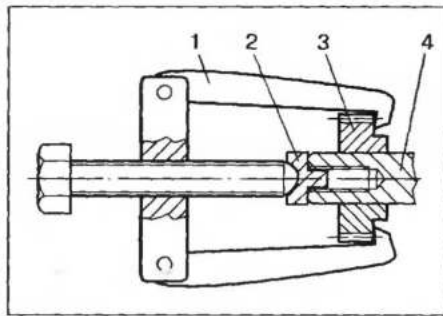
Схема использования съемника для снятия шкивов (звездочек) с хвостовика коленчатого вала:
